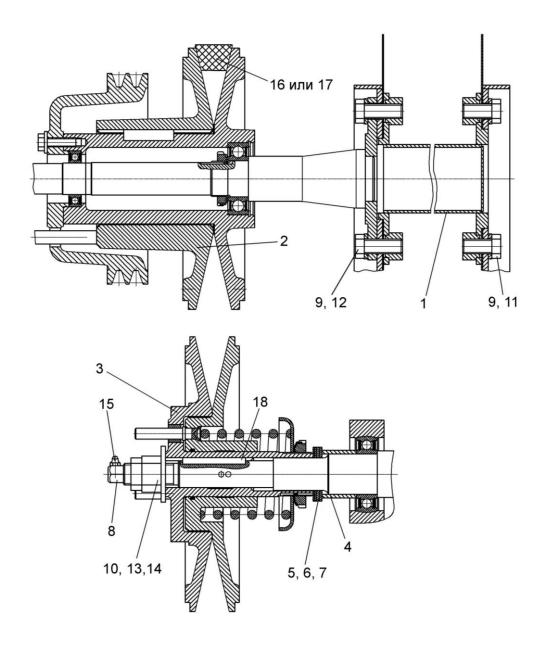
Установка контрпривода вариатора КЗК-12-0202500А и шкива ведомого КЗК-12-0217300
